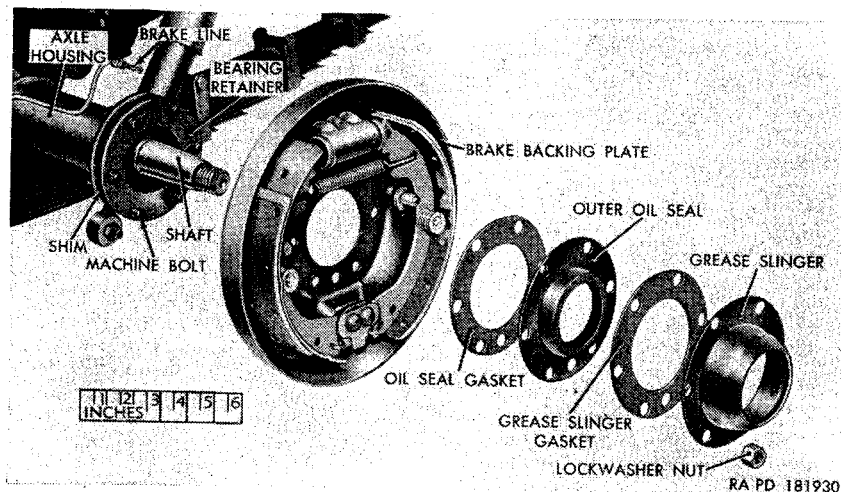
Essieu arrière avec plateau support de frein et les segments, en partie désassemblé
